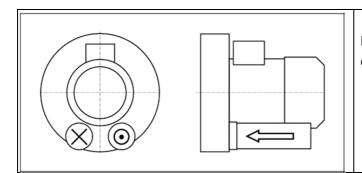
Вакуумный насос/компрессор с одним рабочим колесом.
